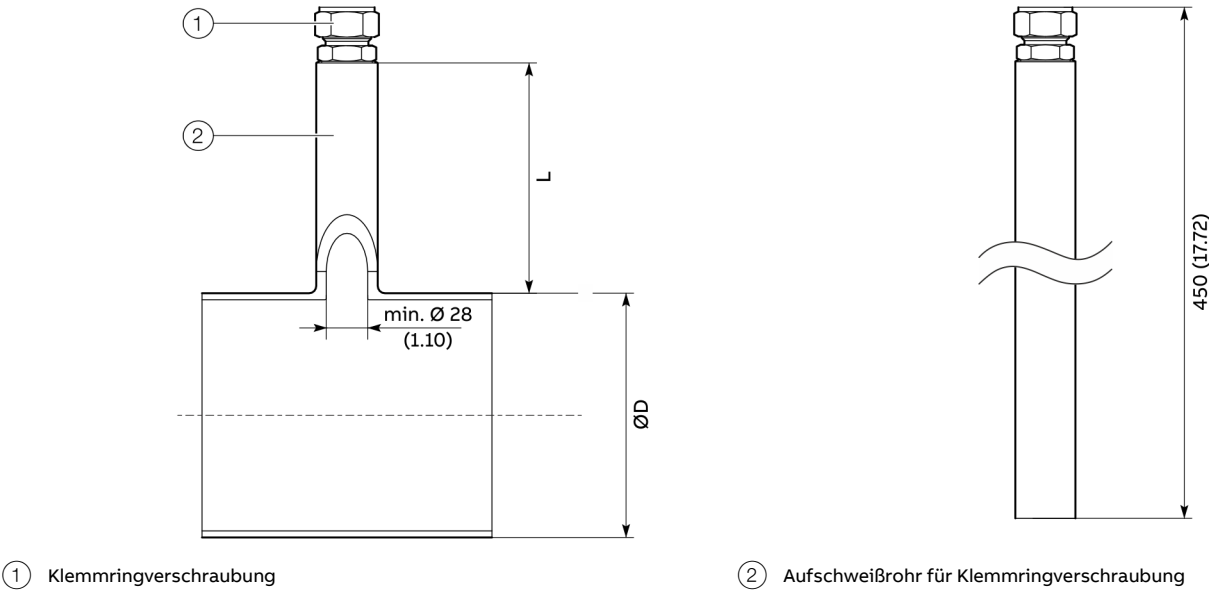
Aufschweißadapter mit Klemmringverschraubung
